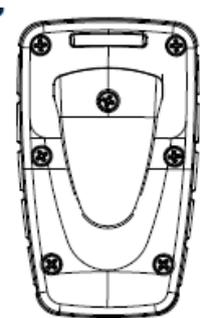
Couvercle de la batterie et les vis verrouillent le couvercle
